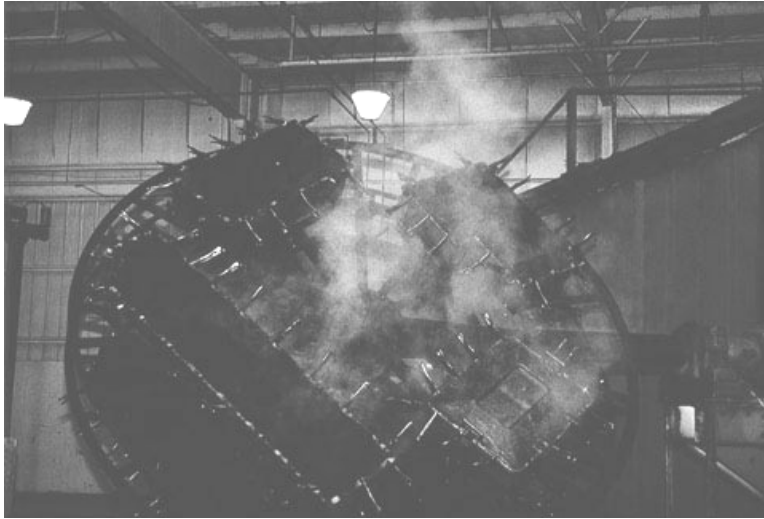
Enfriamiento del molde (imagen tomada de Gold Shield Inc.).
